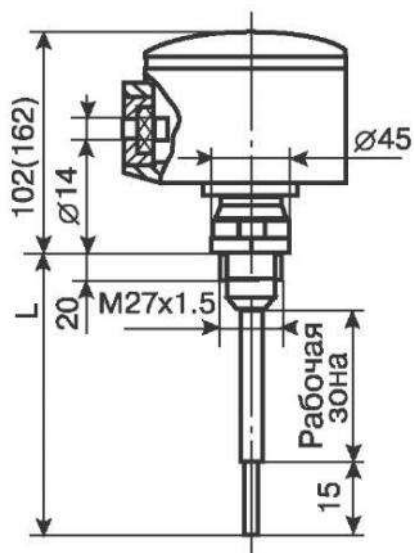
Общий вид, габаритные и установочные размеры СУС-113Р(Б)
